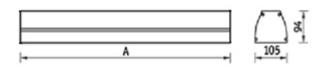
Габаритные размеры светильника с крышками для одиночной установки
